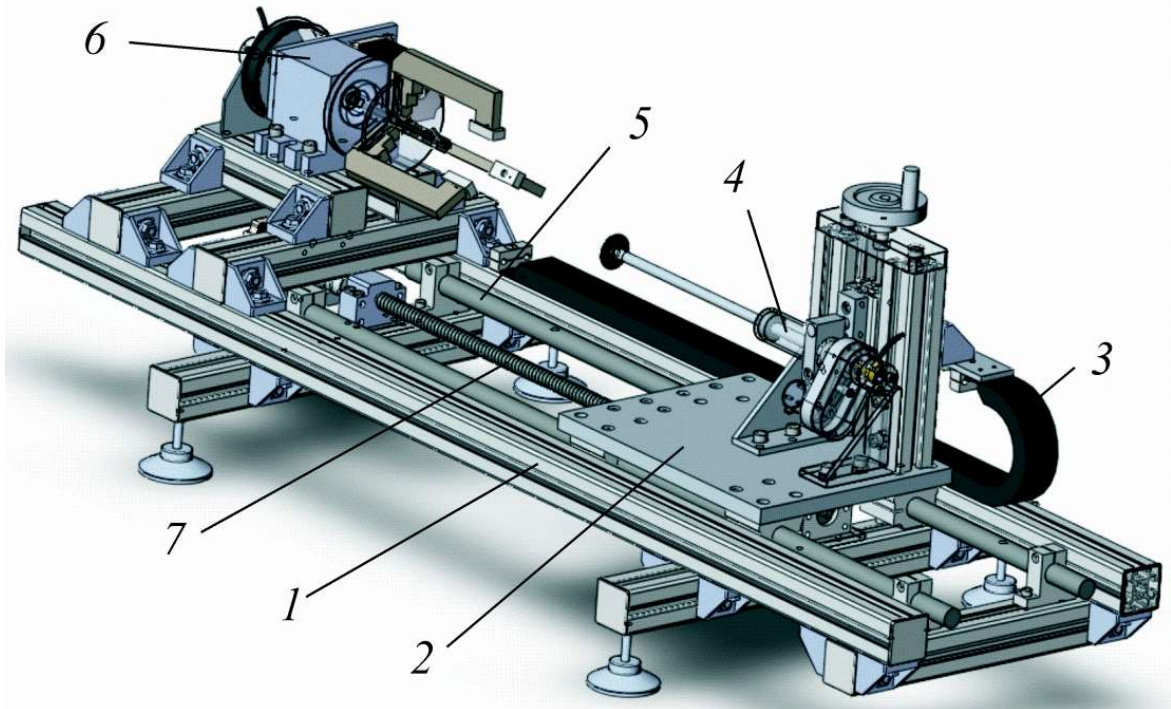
3D модель установки: 1 – каркас; 2 – суппорт; 3 – гибкий провод; 4 – наносящая головка; 5 – направляющие; 6 – поворотная ось; 7 – ходовой винт привода суппорта
